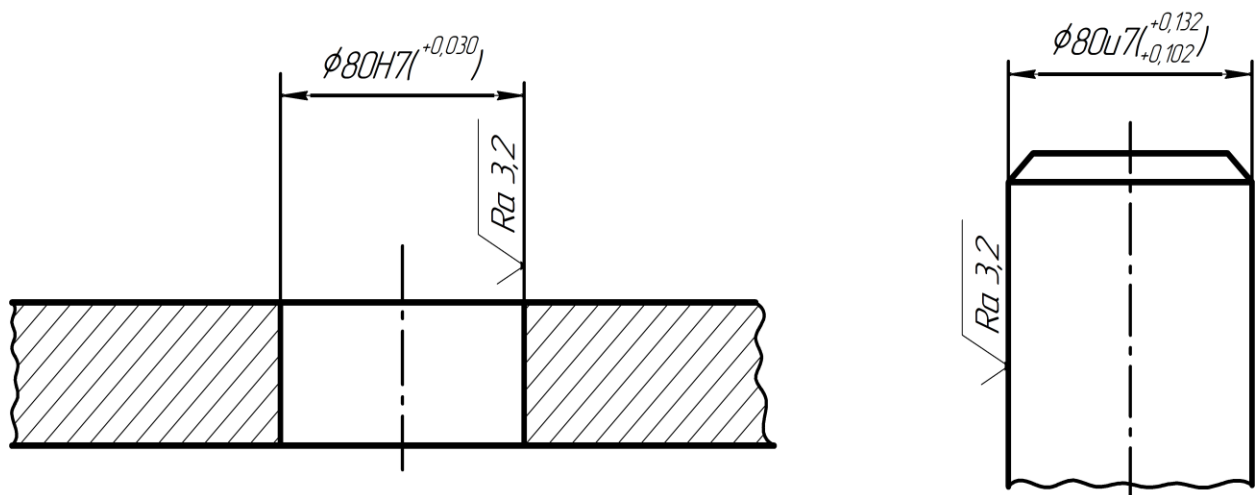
Обозначение допусков размеров на детализовочных чертежах
